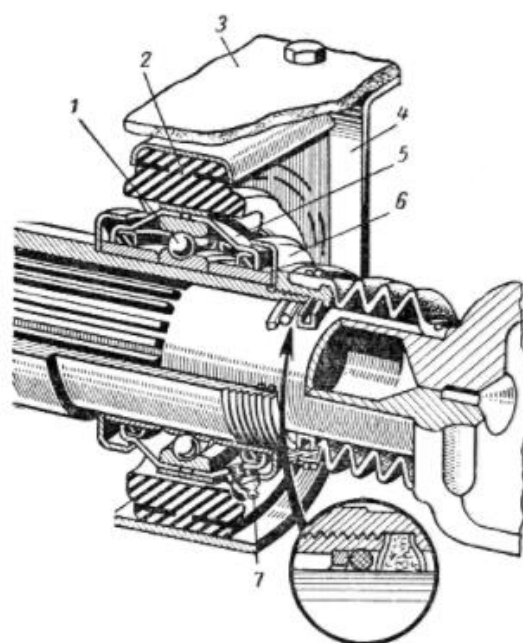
Промежуточная опора с упругим элементом: 1 – шариковый подшипник; 2 – резиновая подушка; 3 – поперечная балка; 4 – кронштейн; 5 – крышка подшипника; 6 – грязеотражатели; 7 – масленка
